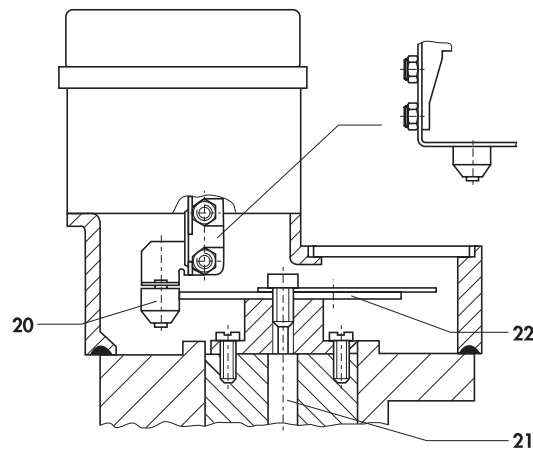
Transmisión del movimiento rotativo al posicionador
